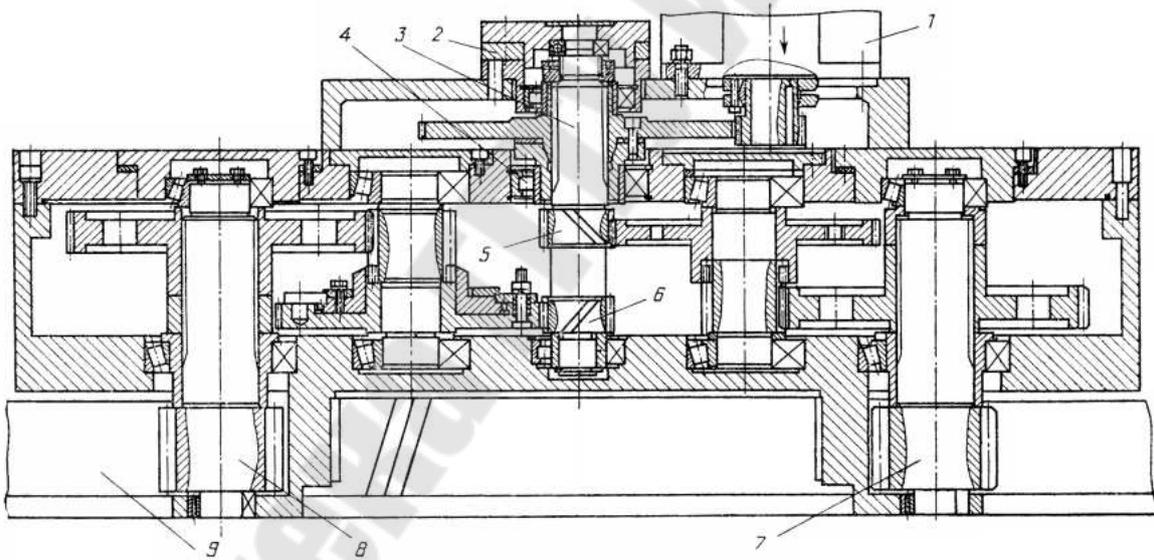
Конструкция привода подачи с тяговым устройством зубчатое колесо-рейка:
